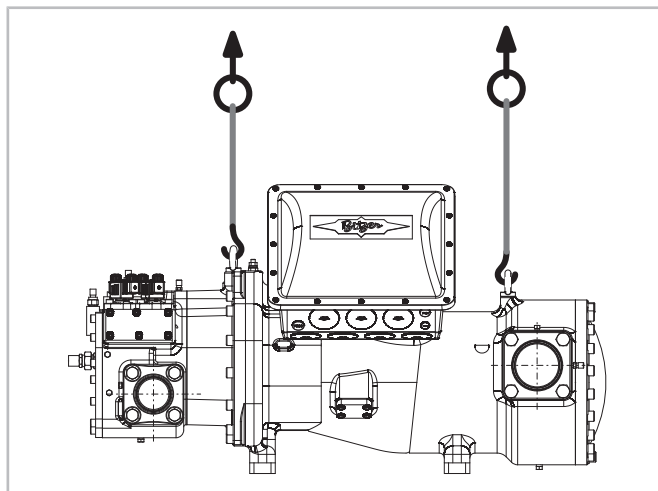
Standard: Soulever les compresseurs, suspension à deux points : Exemple HS.85
